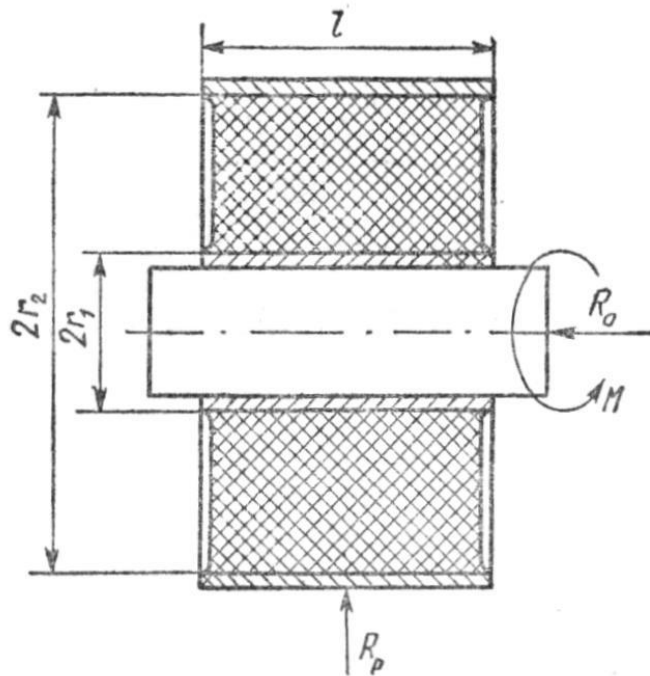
Розрахункова схема гумово-металевого шарніра
